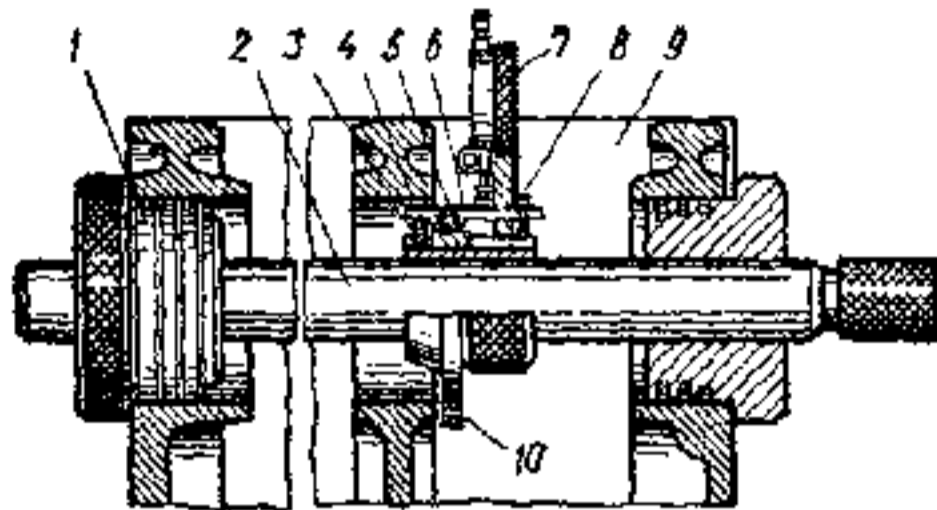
Пристосування для перевірки співвісності отворів у блок-картері під корінні підшипники: 1 - втулка; 2 - оправка; 3 - пружина; 4 - сферичний палець; 5 - вісь; 6 - важіль; 7 - індикатор годинного типу; 8 - регулювальний гвинт; 9 - блок; 10 - упорний штифт
